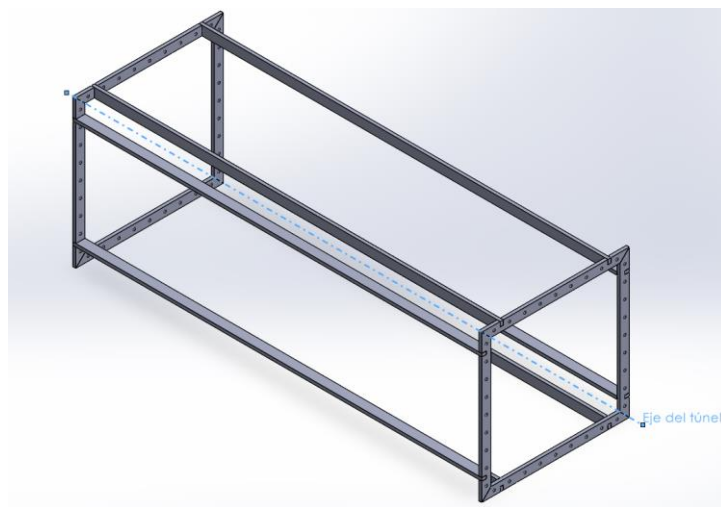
Estructura de la zona de ensayo. Formato CAD.
